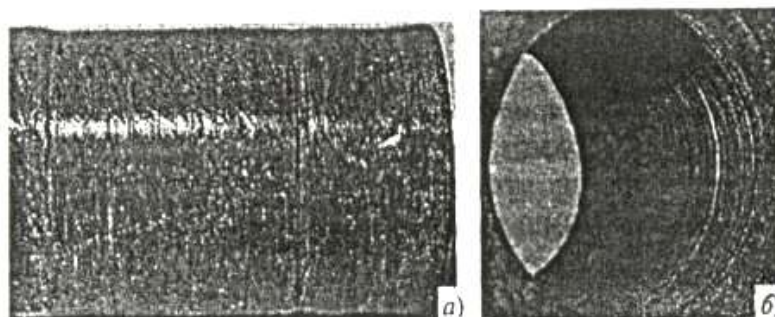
Поверхности втулок вала (а) и подшипника (б) НЦС-01 после испытаний
